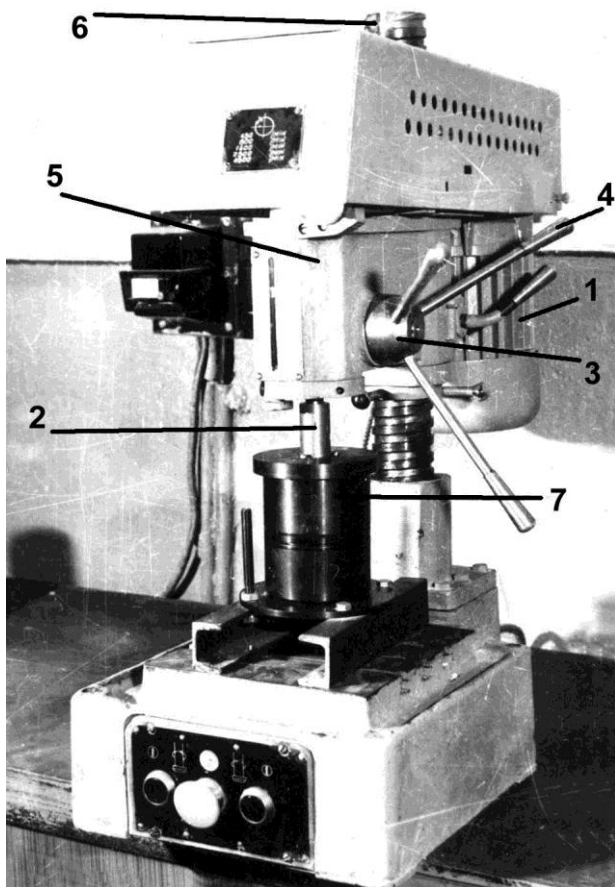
Загальний вид експериментальної установки для випробувань на зношування на базі свердлувального верстата:
